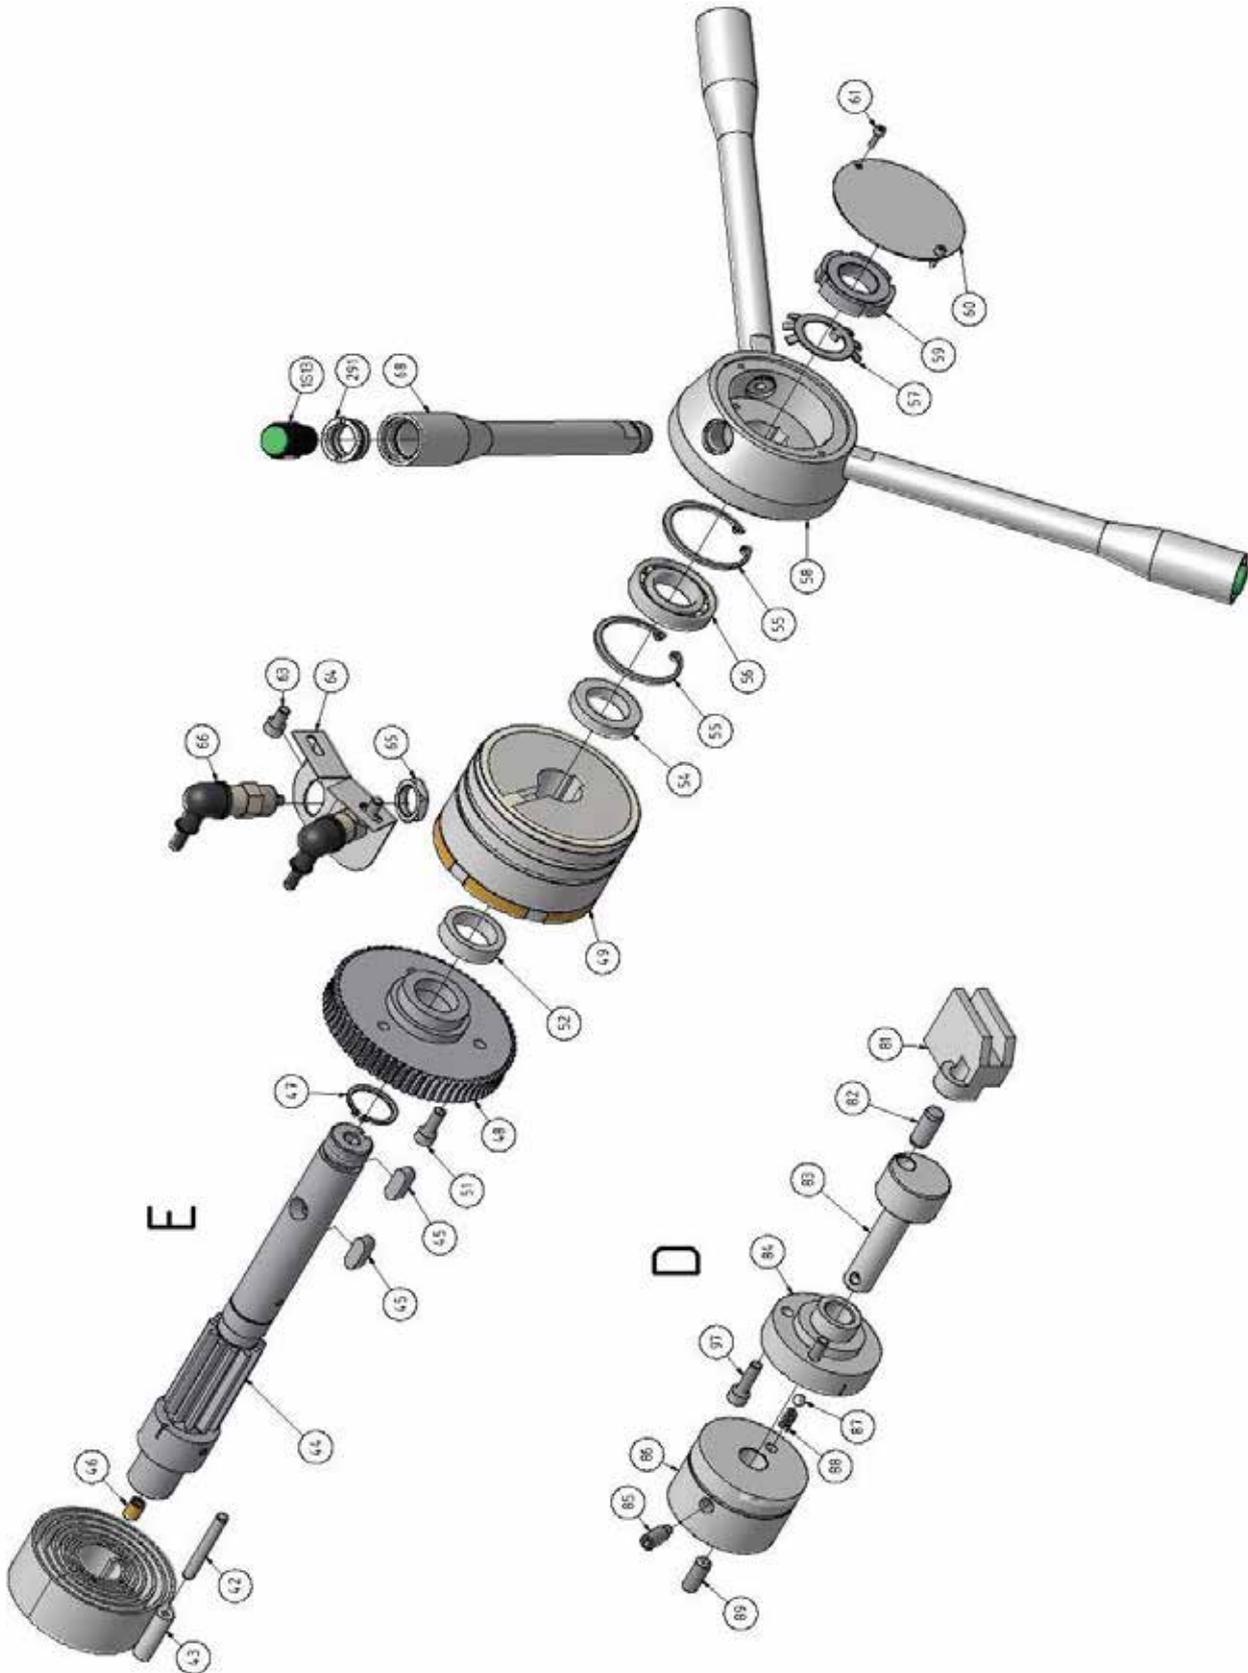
Vorschubgetriebe 2 von 4 - Feed gear box 2 of 4
